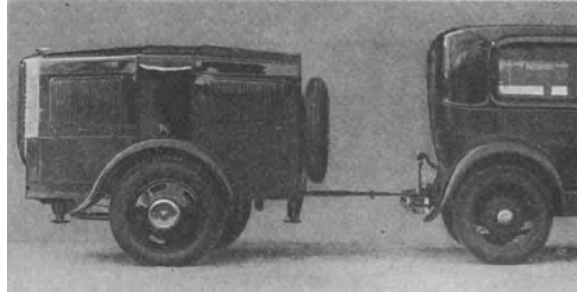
Schweißgenerator mit Benzinmotorantrieb („Schweißwagen“).
